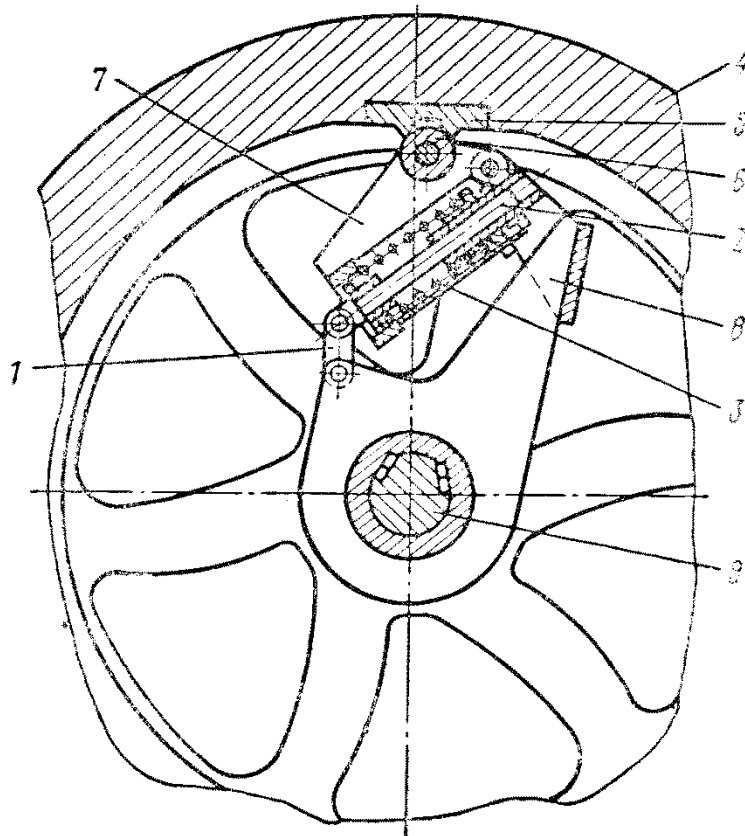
Схема запобіжного пристрою щоків дробарки зі складним рухом щоки на шків-маховику установки:
